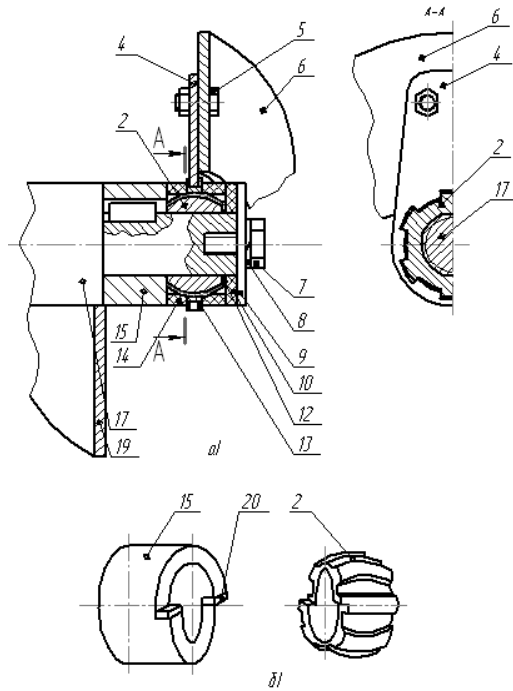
Пристрій для кріплення шнеку до вала і ескіз втулки вид б)
